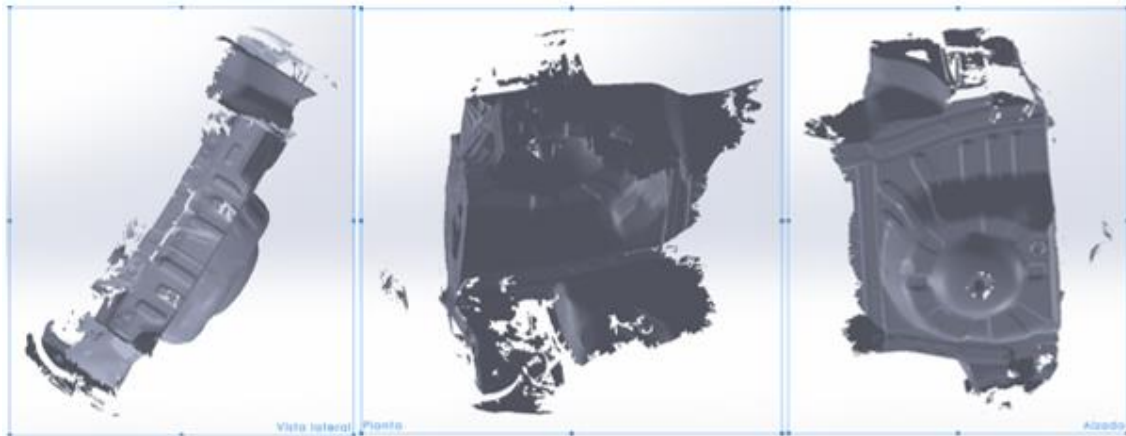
Vista lateral, planta y alzado del archivo en bruto
